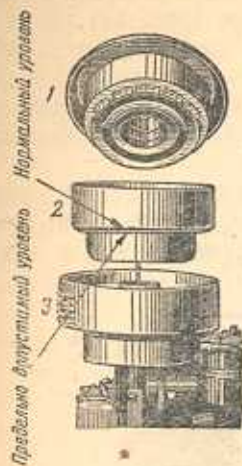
Воздушный фильтр карбюратора: 1—сетчатый фильтрующий цилиндр; 2—масляный резервуар; 3—корпус
